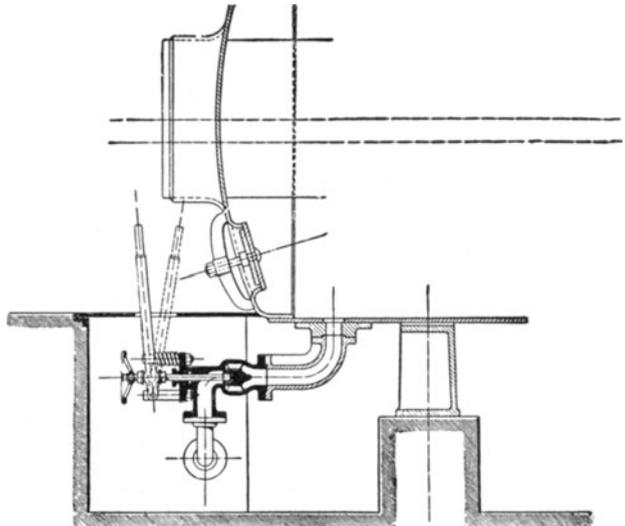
Abschlämmventil mit Handhebel an einem Flammrohr von der Dinglerschen Maschinenfabrik A. G. in Zweibrücken.
